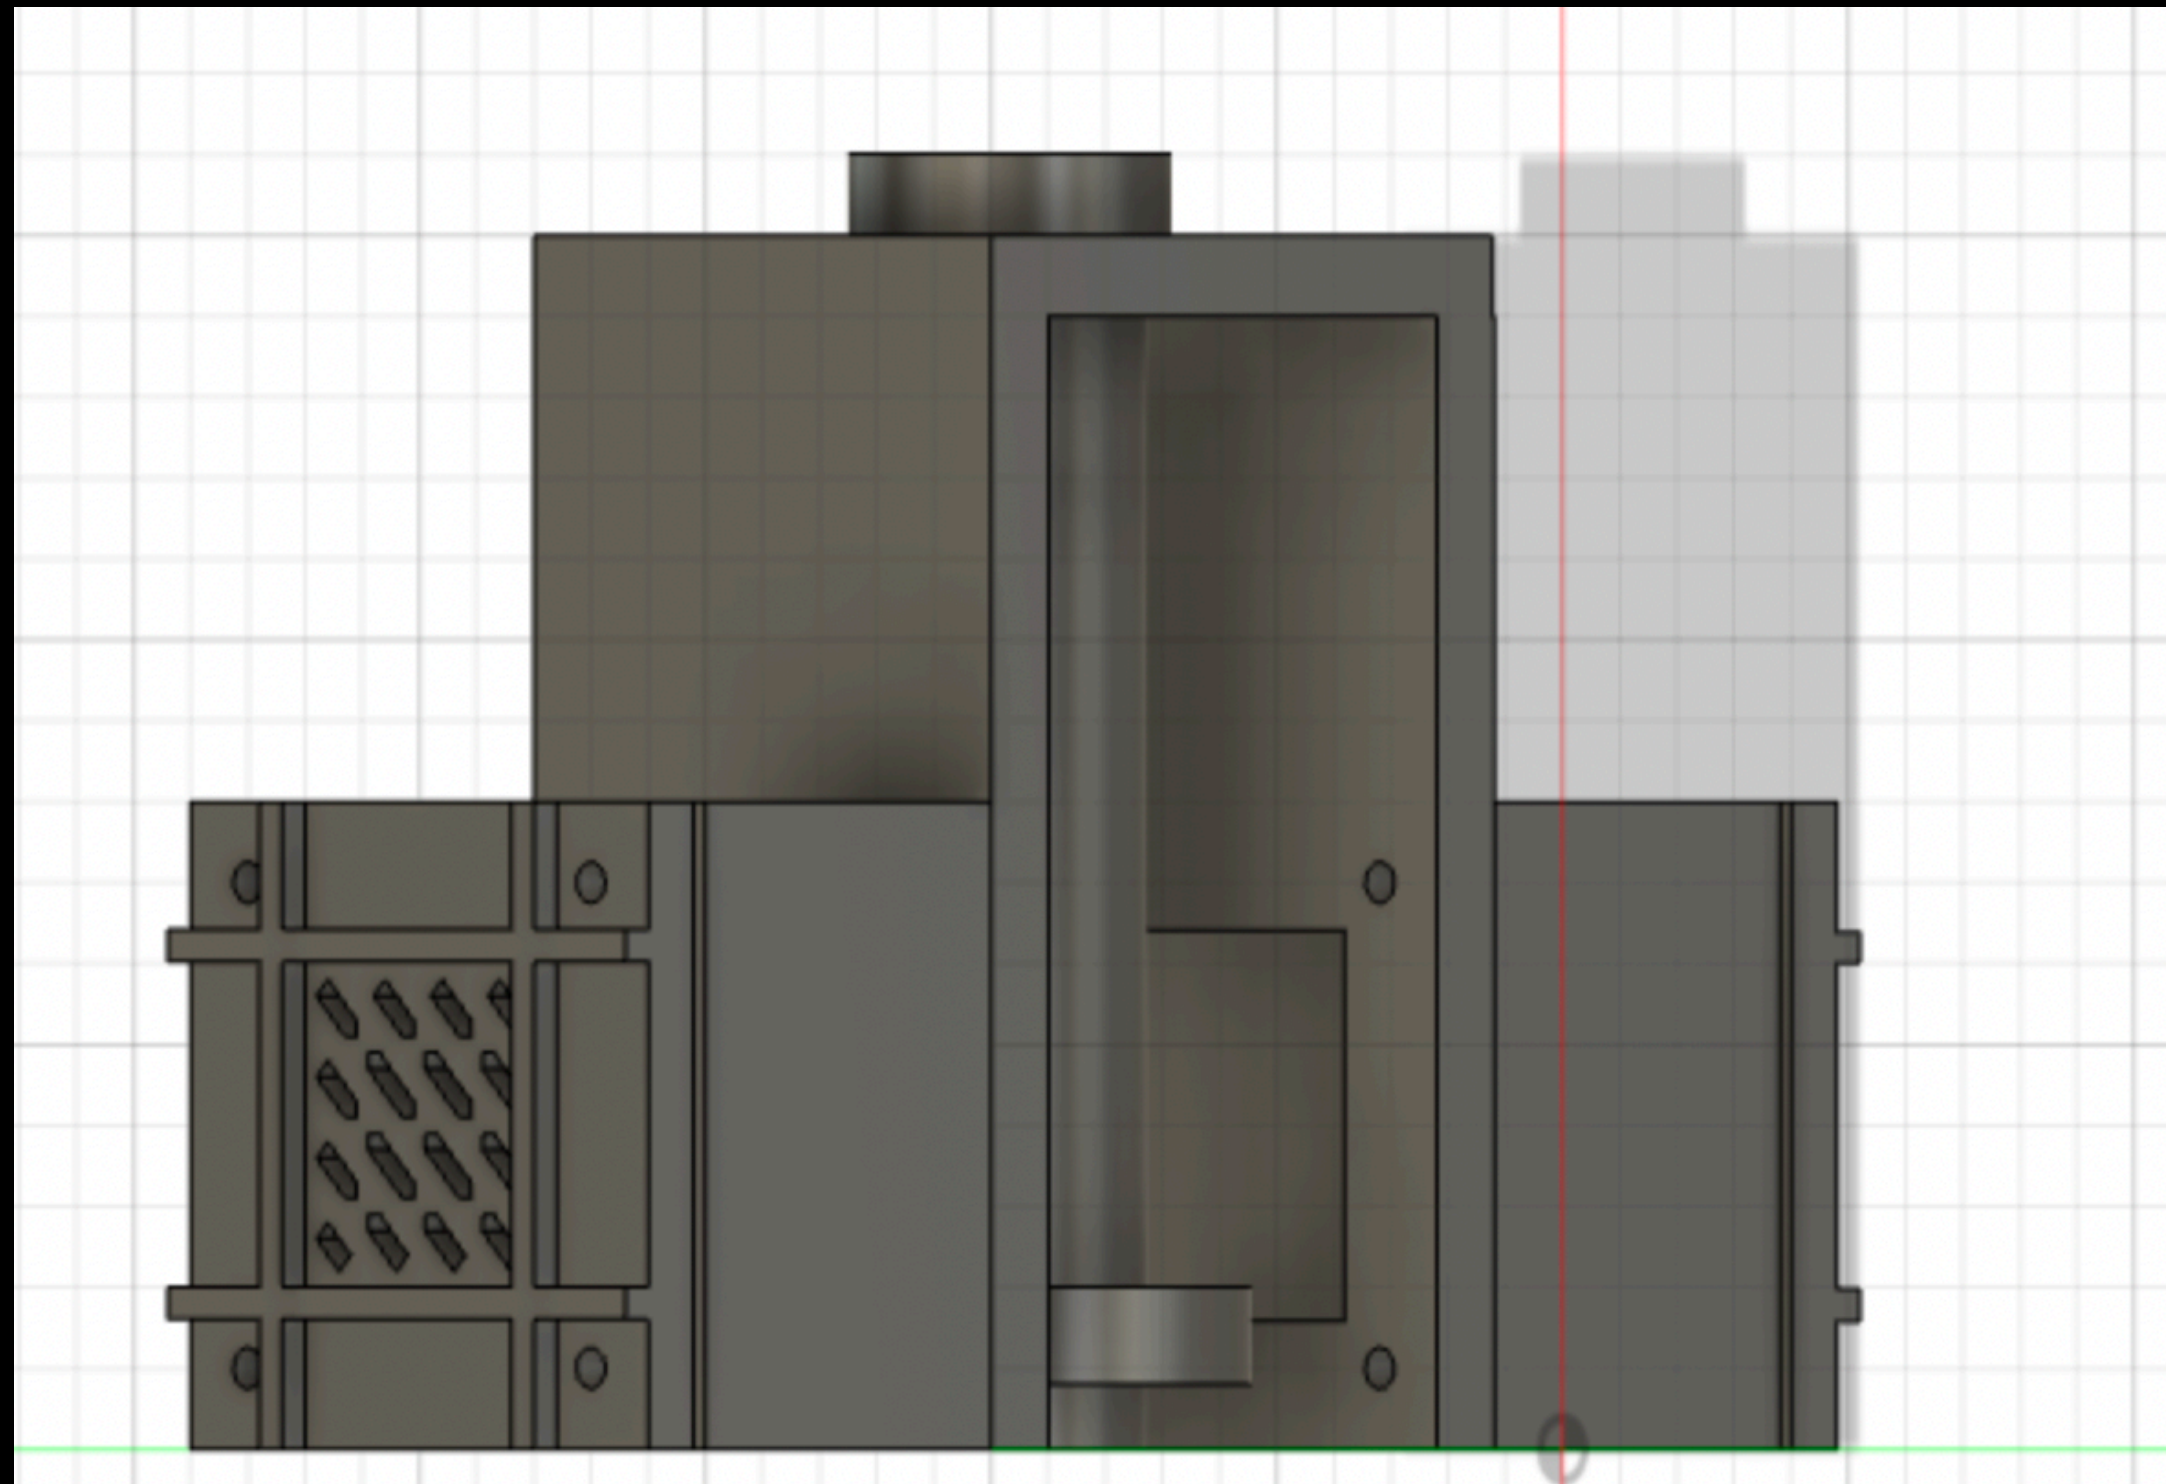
Разработанный для фотополимерной печати корпус ПЭТ
